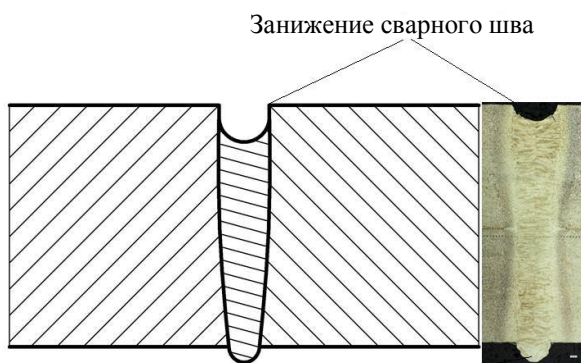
Дефект лазерной сварки с глубоким проплавлением – занижение сварного шва
